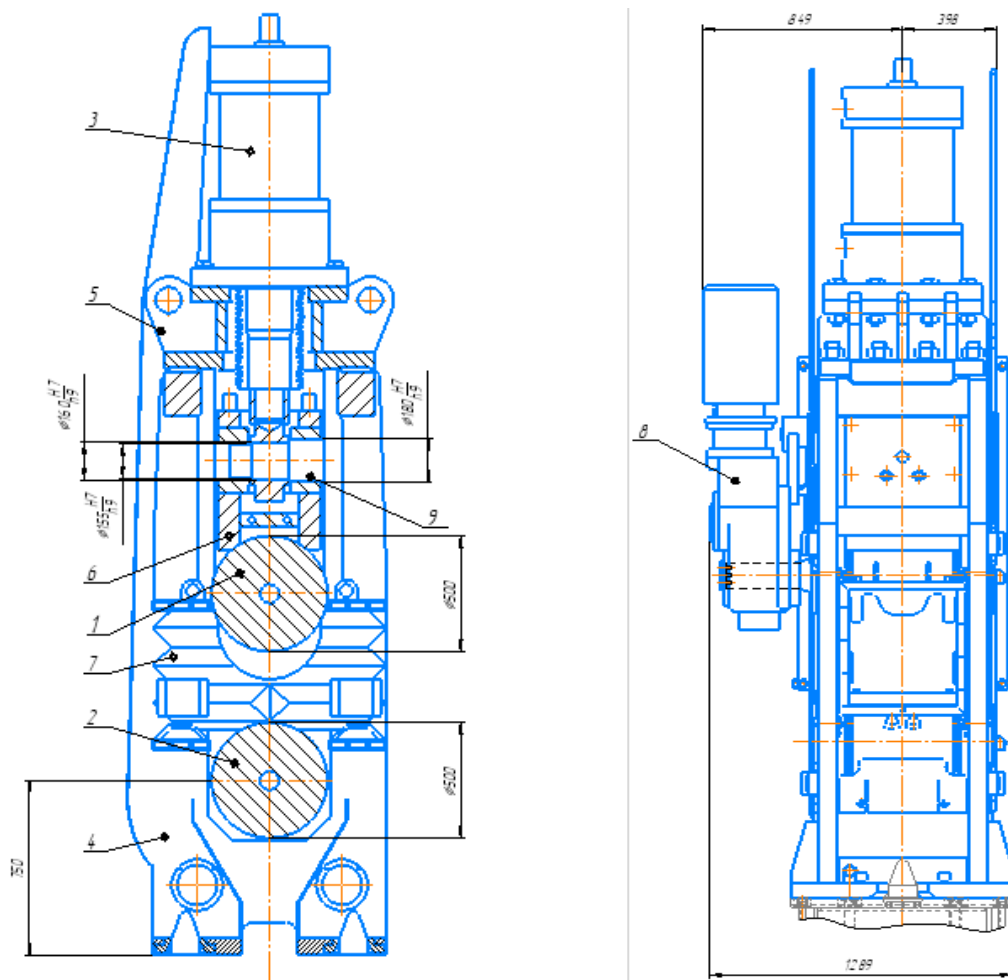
Конструкция ТПА: 1 – приводной ролик; 2 - холостой ролик; 3 – гидроцилиндр; 4 – станина; 5 – фланец; 6 – прижимной механизм; 7 – рубашка охлаждения; 8 – мотор-редуктор; 9 – палец гидроцилиндра
